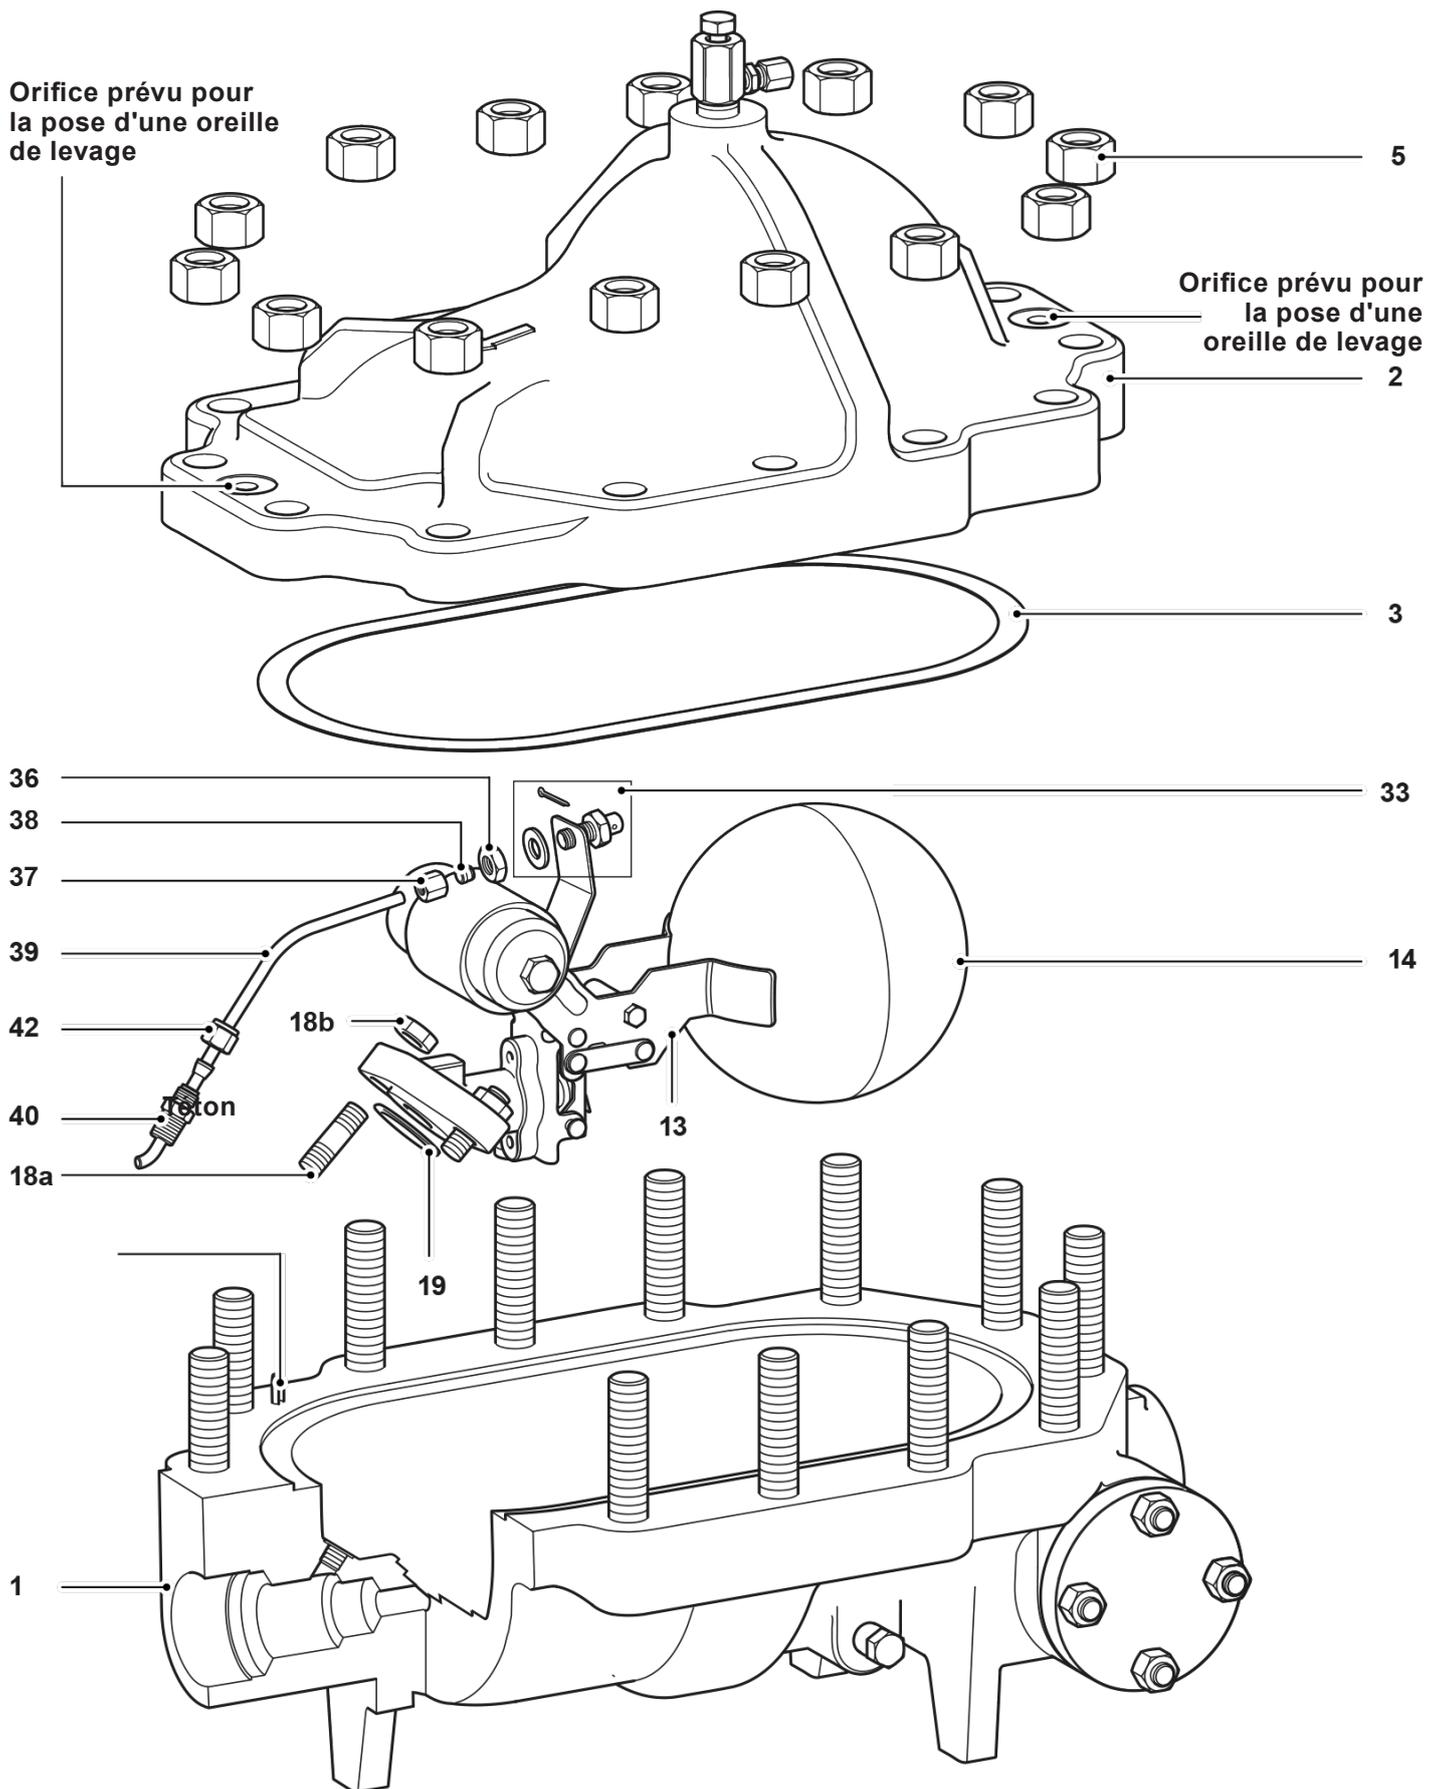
Remplacement de l'ensemble tube évent et mécanisme/flotteur
